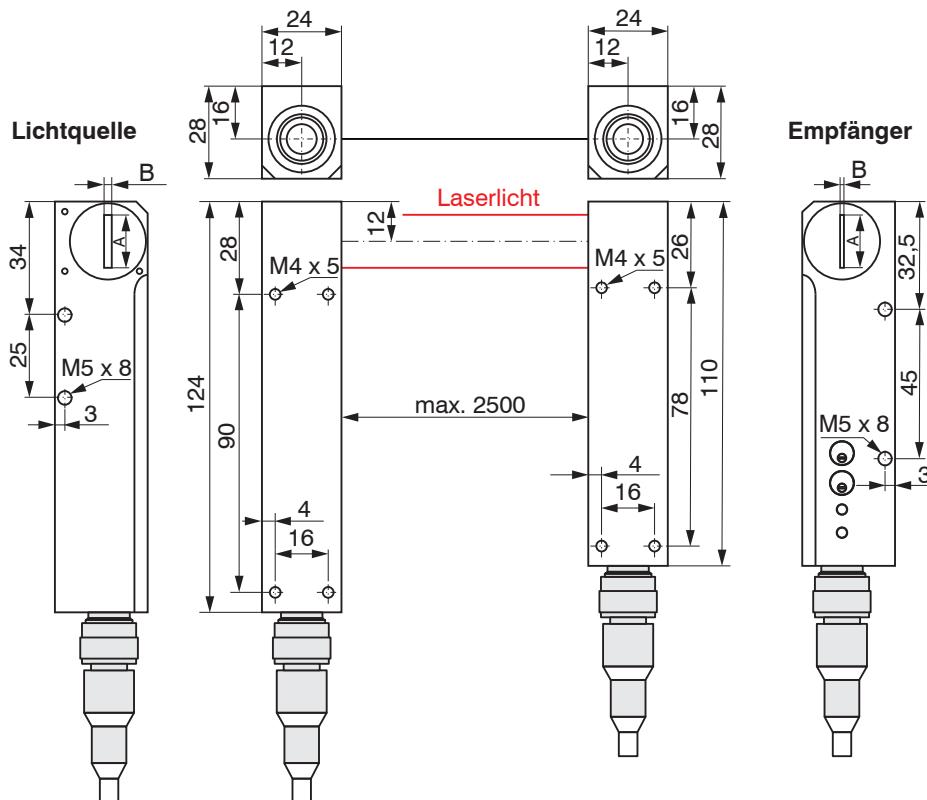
Maßzeichnung ODC 1200/90, Abmessungen in mm
